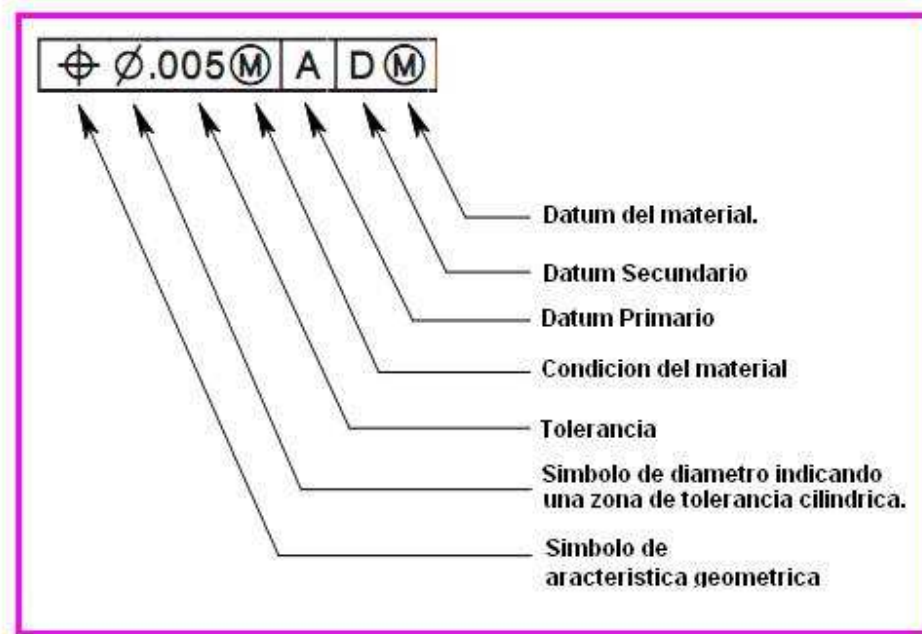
Rectángulo de tolerancias geométricas.
